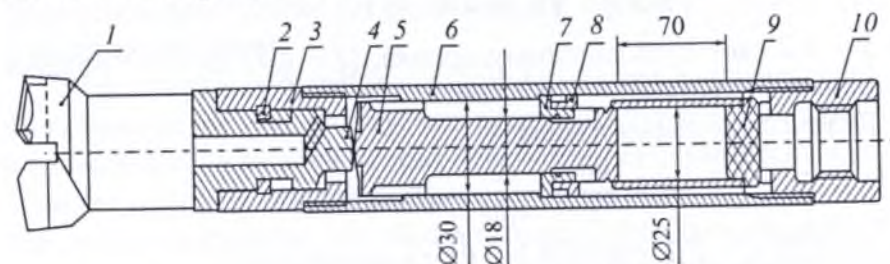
Пневмоударник АШ-46А: 1 – буровая коронка; 2 – кольцо; 3 – гайка передняя; 4 – букса; 5 – ударник; 6 – корпус; 7 – втулка разрезная; 8 – гильза; 9 – пробка; 10 – гайка задняя
